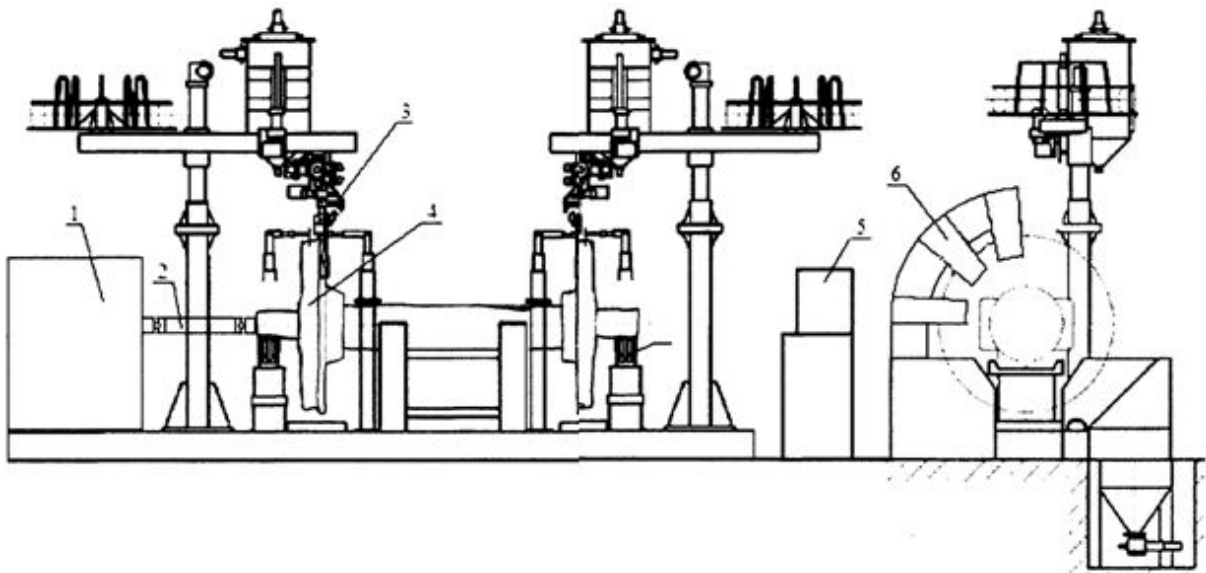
Загальний вигляд пристрою для нагріву реборд колісних пар: 1 — електропривод обертання; 2 — карданний вал; 3 — зварювальна установка; 4 — колісна пара; 5 — блок керування нагрівачем; 6 — індукційний нагрівач
